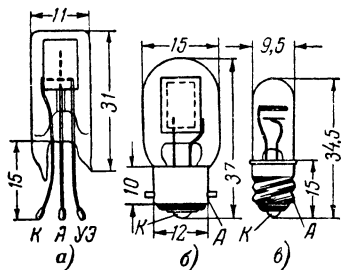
Внешний вид газоразрядных приборов и их цоколевка.
